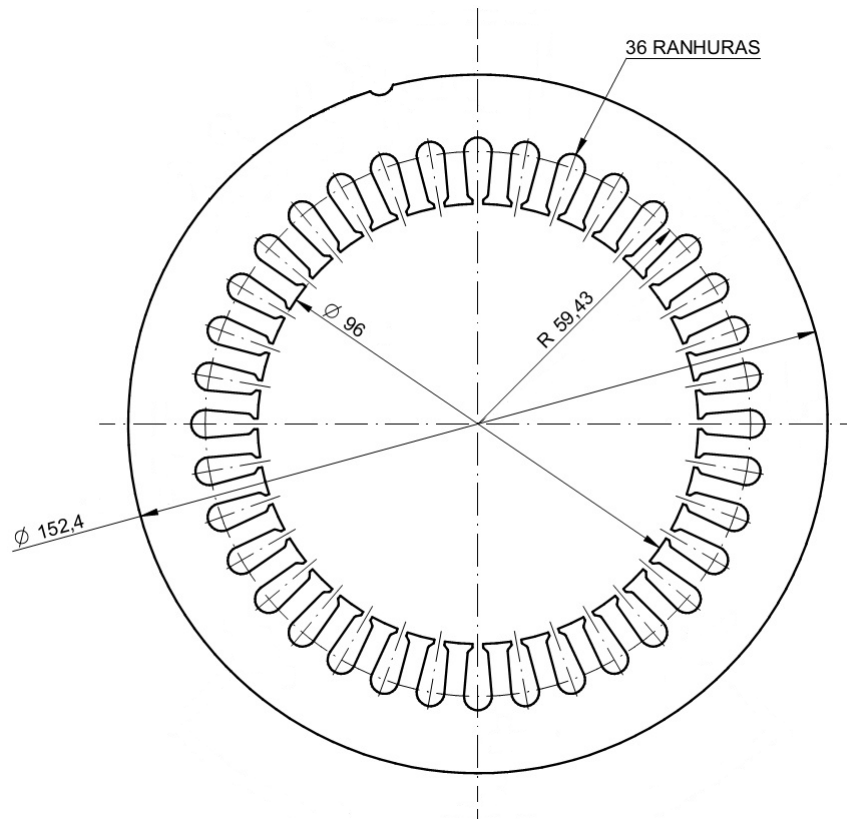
Desenho com as dimensões do estator da máquina de indução original.
